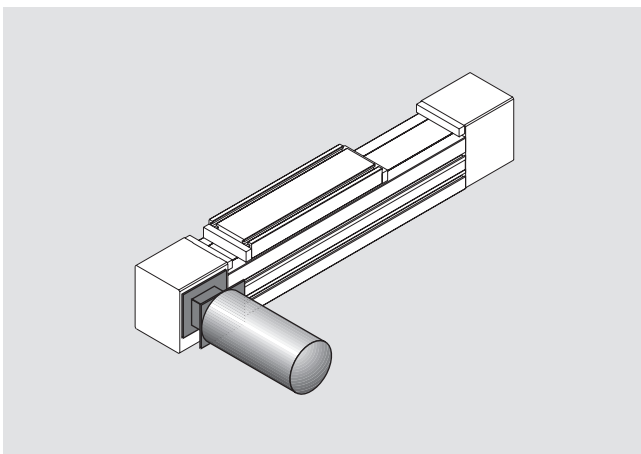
Zahnriemenantrieb links mit Kupplung und Zwischenflansch (Montagezustand 14)
